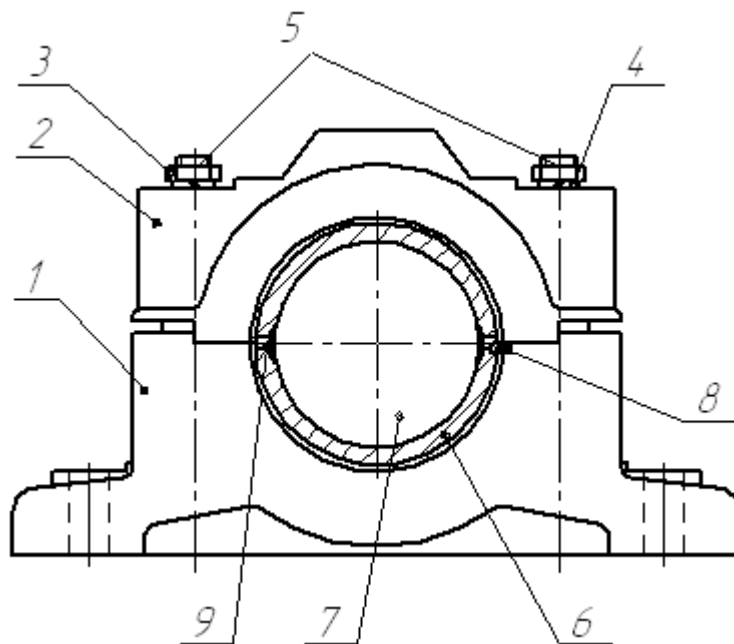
Подшипник скольжения с разъемным корпусом: 1 – корпус; 2 – крышка корпуса; 3 – гайка; 4 – пружинная шайба; 5 – шпильки; 6 – вкладыш; 7 – вал; 8 – закрепительная втулка; 9 – карман маслоподводящий для жидкой смазки гладких вкладышей
